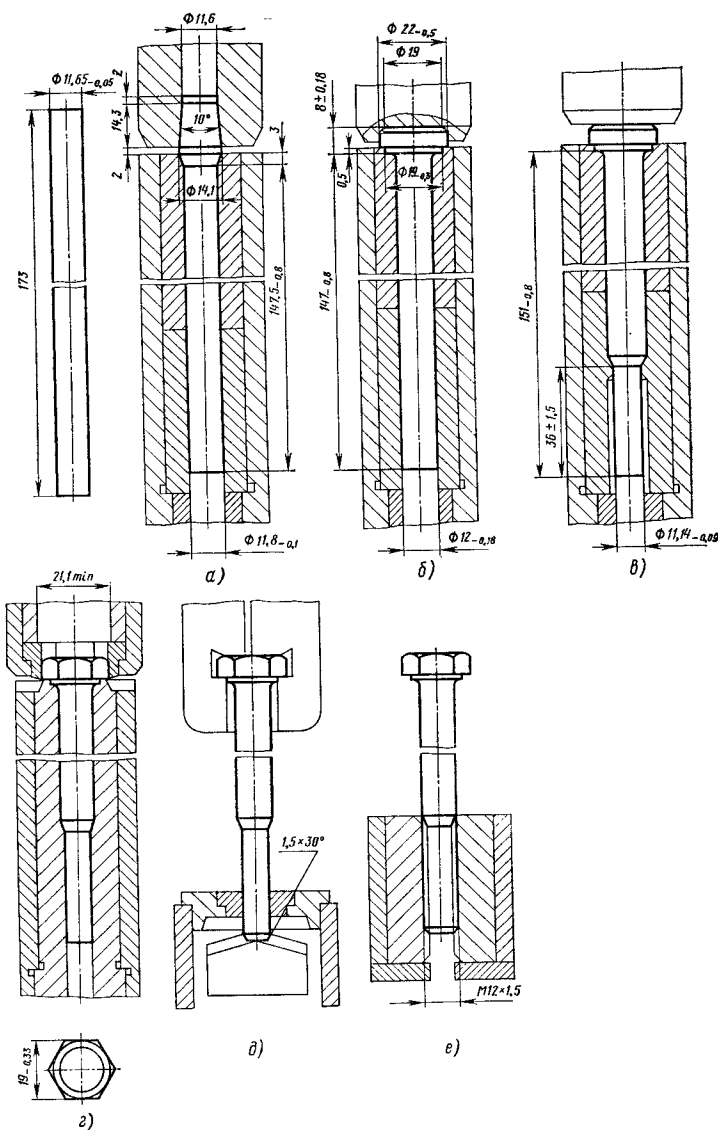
Переходы и наладка рабочего инструмента при штамповке болта с образованием граней обрезкой на четырехпозиционном автомате с устройствами для подрезки торца и накатки резьбы:
